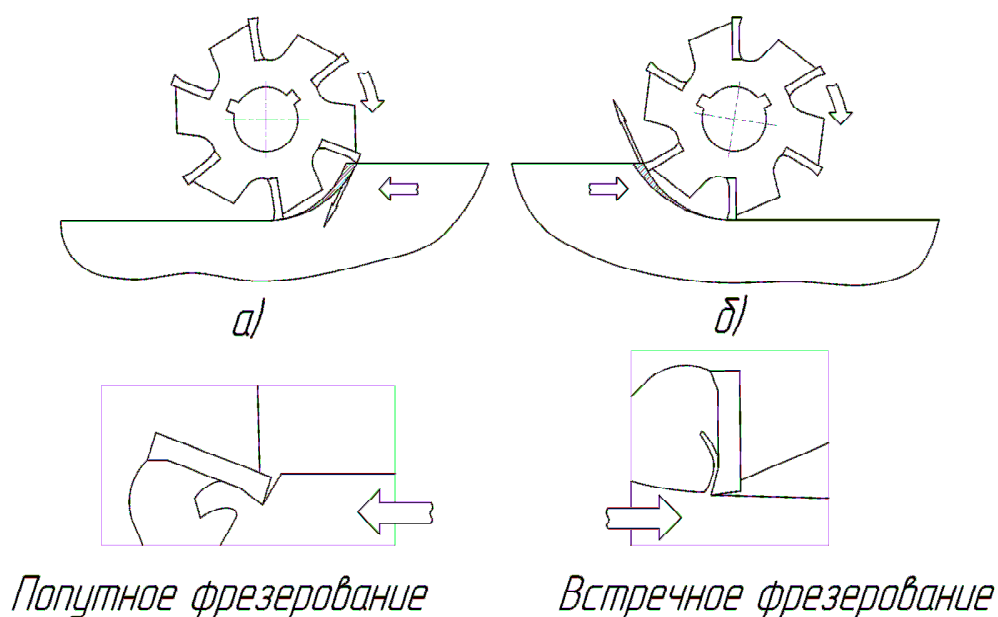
Способы фрезерования, определяемые направлением движения заготовки относительно инструмента; а – попутное фрезерование; б – встречное фрезерование
